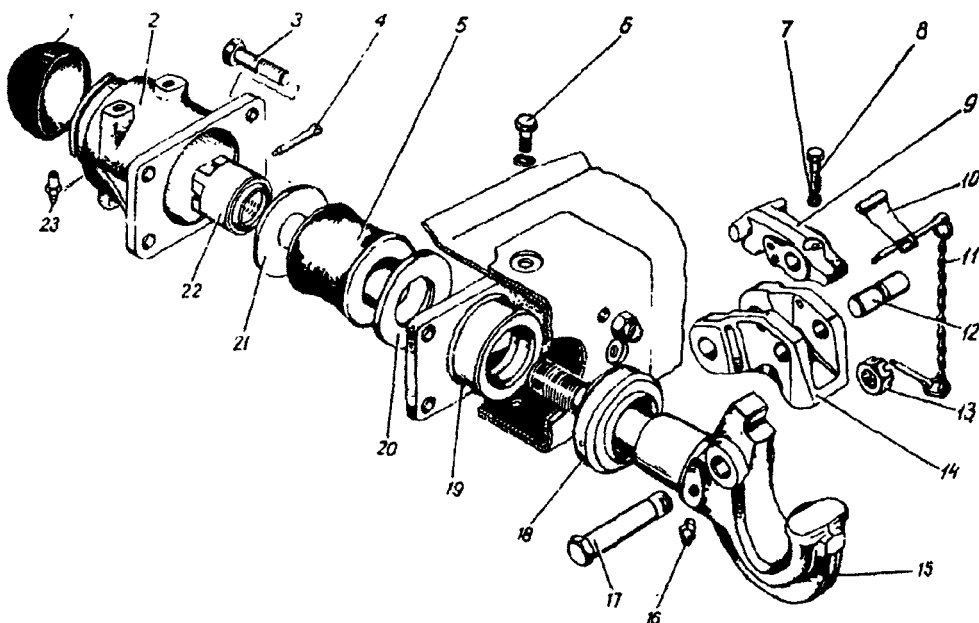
Устройство тягово-цепное: 1 — колпак гайки крюка; 2 — корпус прибора; 3, 6 — болты; 4 — шплинт; 5 — буфер; 7 — шайба; 8 — болт крепления собачки; 9 — собачка защелки; 10 — пружина собачки; 11 — цепь шплинта защелки; 12 — ось собачки; 13 — гайка крепления защелки; 14 — защелка крюка; 15 — крюк; 16, 23 — масленки; 17 — палец защелки; 18 — грязеотражатель крюка; 19 — крышка корпуса; 20 — фланец задний; 21 — фланец передний; 22 — гайка крюка
